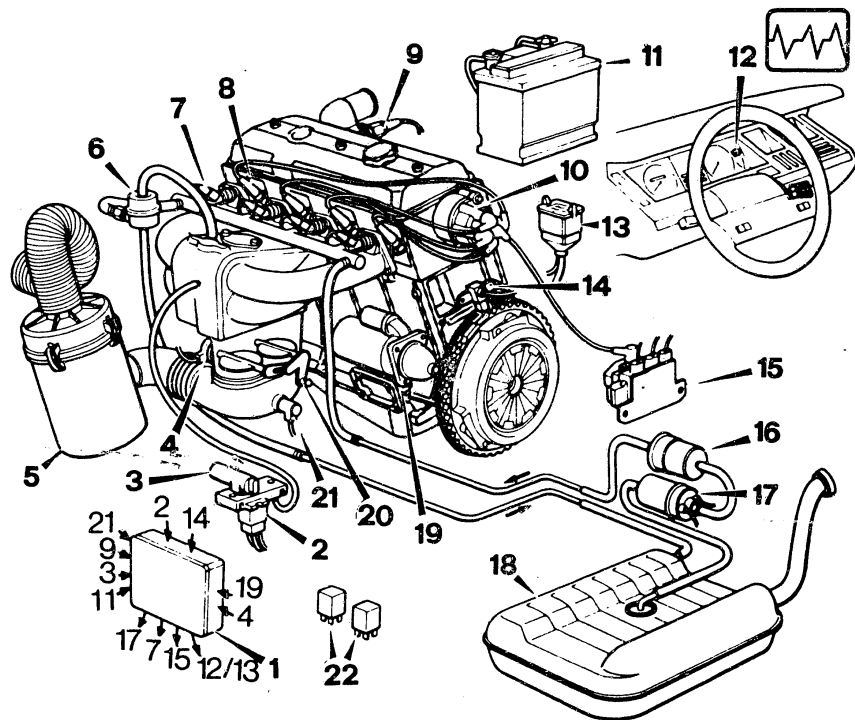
Übersichtsplan der Benzin-Einspritzanlage Renix: 1 Elektronisches Steuergerät für Einspritz- und Zündanlage – 2 Fühler für Saugrohrdruck – 3 Potentiometer für Leerlaufgemisch-Regulierung – 4 Drosselklappenschalter – 5 Luftfilter – 6 Benzin-Druckregler – 7 Einspritzventil – 8 Zündkerze – 9 Temperaturfühler Kühlflüssigkeit – 10 Zündverteiler – 11 Batterie – 12 Störungsanzeige – 13 Diagnose-Zentralstecker – 14 Impulsgeber – 15 Zündleistungsmodul – 16 Benzinfilter – 17 Benzinpumpe – 18 Benzintank – 19 Anlasser – 20 Drosselklappengehäuse – 21 Temperaturfühler Ansaugluft – 22 Relais für Benzinpumpe und Steuerung der Einspritzanlage.
